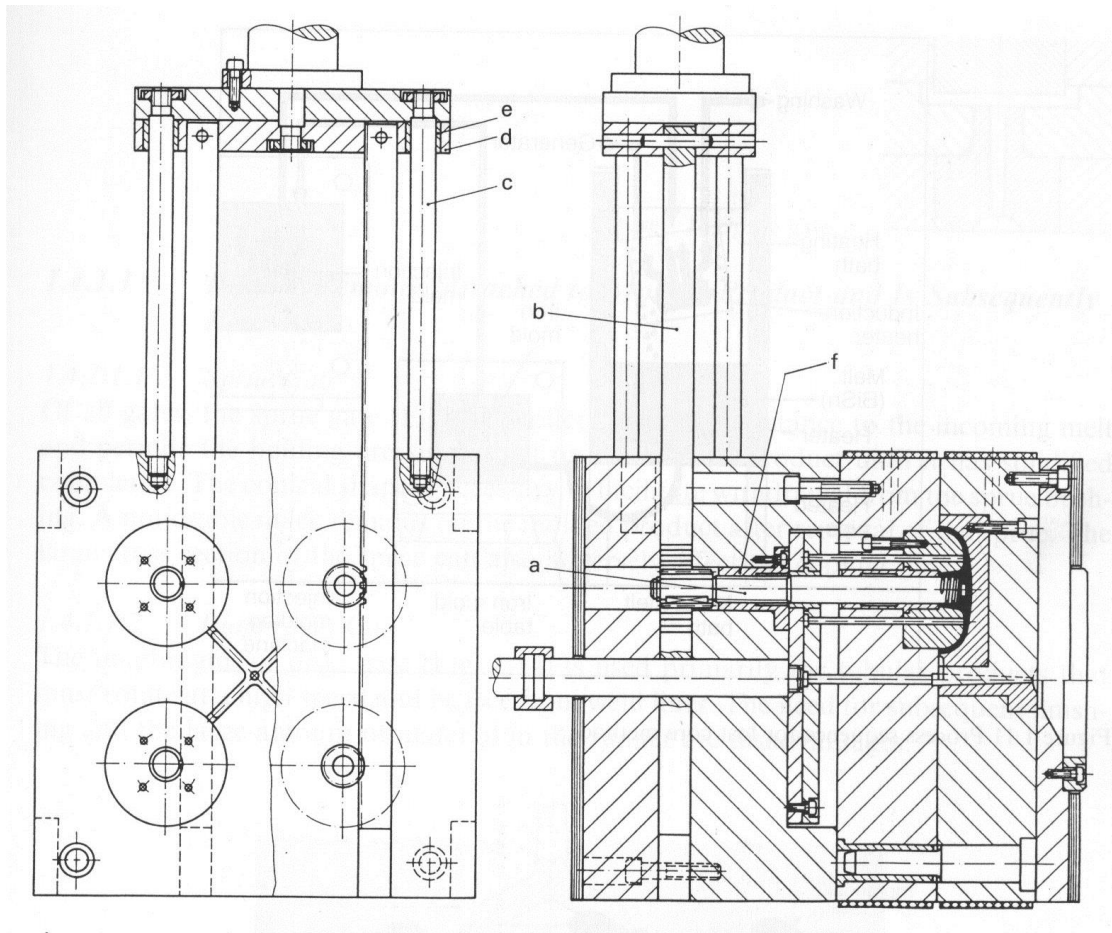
Molde de cuatro cavidades para partes roscadas accionado por cremallera.
